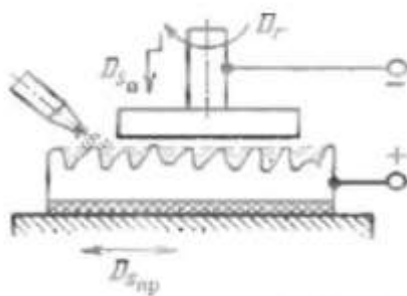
Схема анодно-механічної обробки плоскої поверхні.
